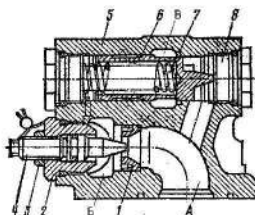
Регулятор расхода масла: 1 – дроссель; 2 – корпус регулировочного винта; 3 – гайка; 4 – регулировочный винт; 5 – корпус регулятора; 6 – глукер; 7 – пружина; 8 – м-проба; А – напорный канал от насоса; Б – напорный канал к усилителю (приоритетному клапану); В – канал подачи масла на радиатор.
